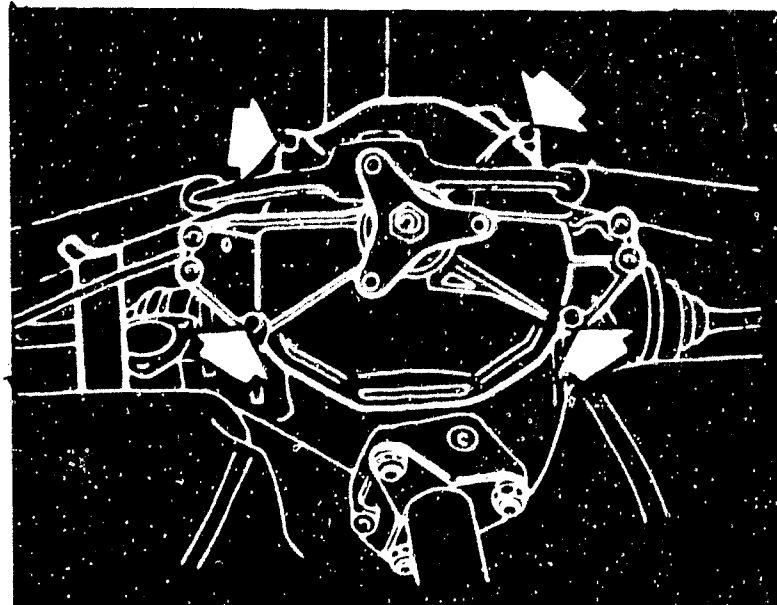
Nach dem Lösen der 4 Schrauben (Pfeile) lässt sich das komplette Kupplungsaggregat ausbauen.
